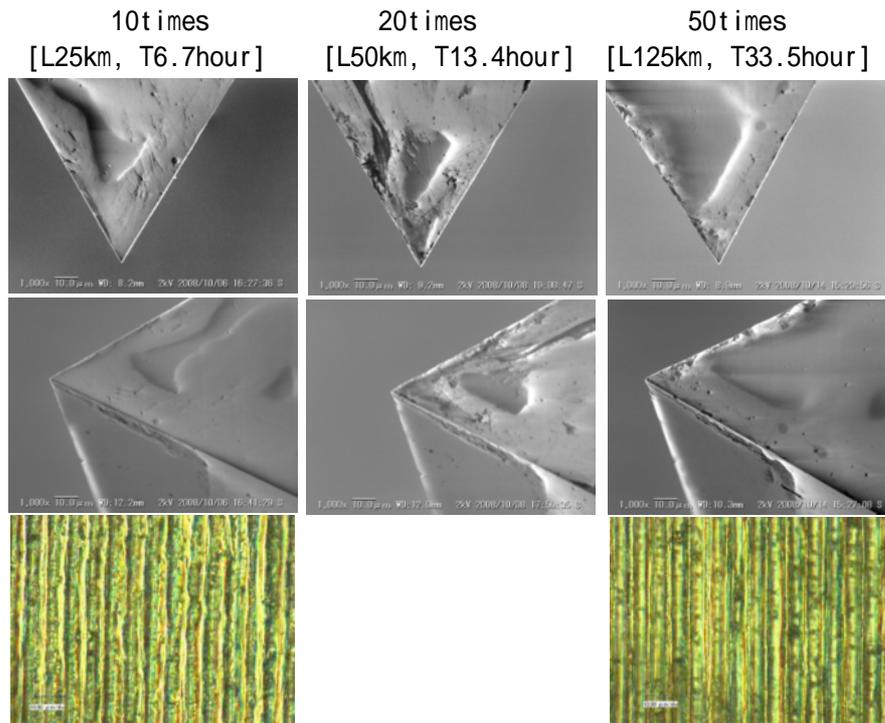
[Tool 2]の工具摩耗と加工面性状
